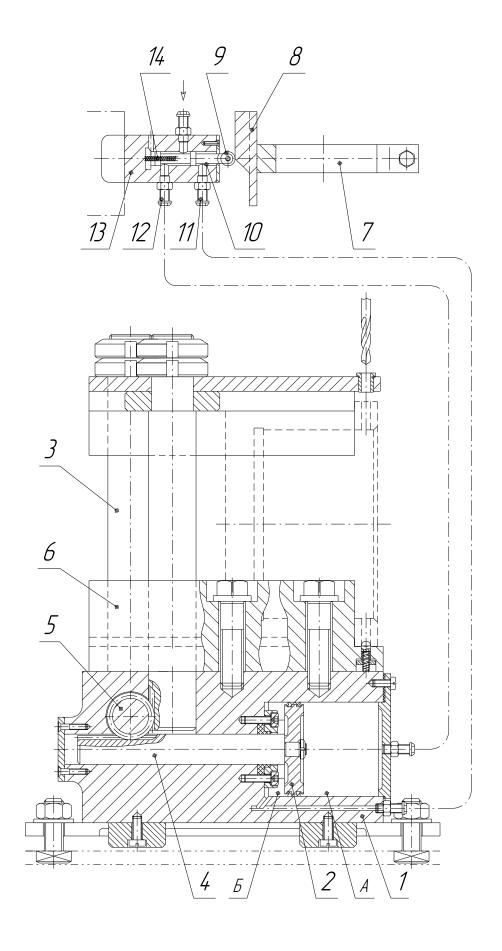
Скальчатый кондуктор с пневмоприводом для автоматизированного зажима и раскрепления деталей
